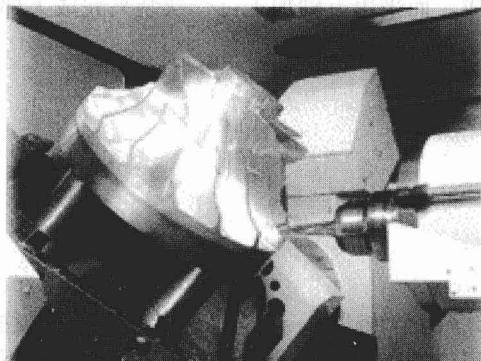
工作台回转的卧式五轴加工中心加工叶轮
